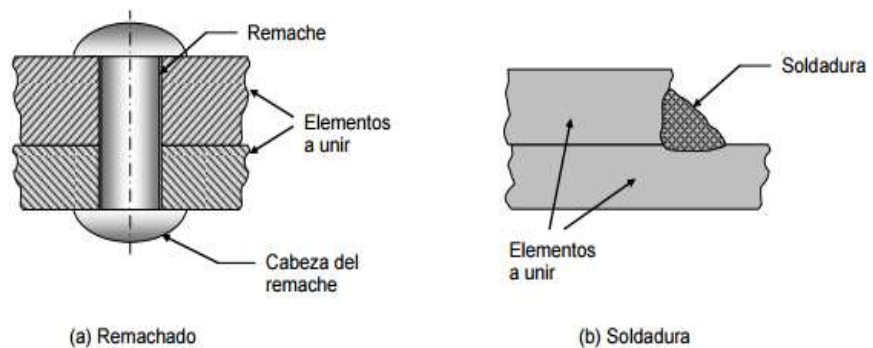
remachado y soldadura, Fuente: libro conceptos básicos sobre diseño de máquinas
